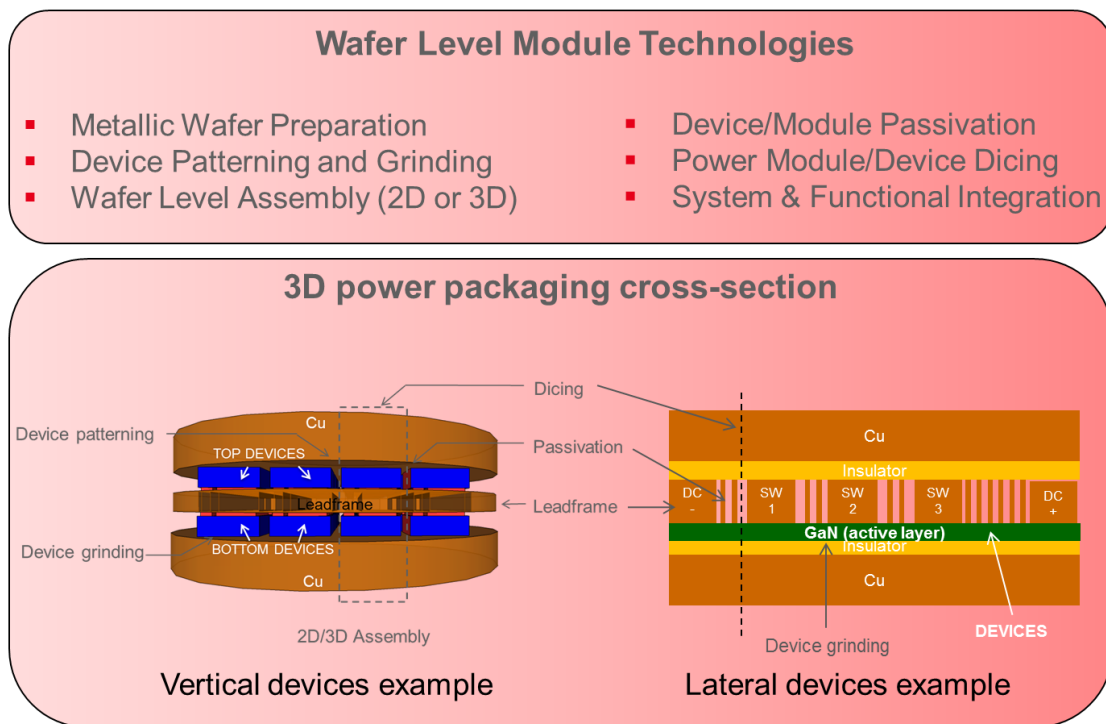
Modules 3D assemblés à l'échelle de la plaque par des procédés collectifs regroupant un leadframe, une ou deux plaques de composants actifs, ainsi que des plaques métalliques massives pour les faces arrière
